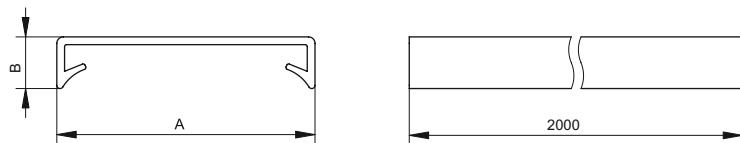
Размеры крышки / Figure 2 – Cover dimensions / 2-сурет – Қақпақ өлшемдері
